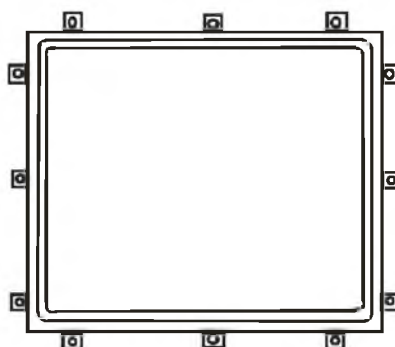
Схема крепления уплотняющего шланга и уголков затяжки двери.
